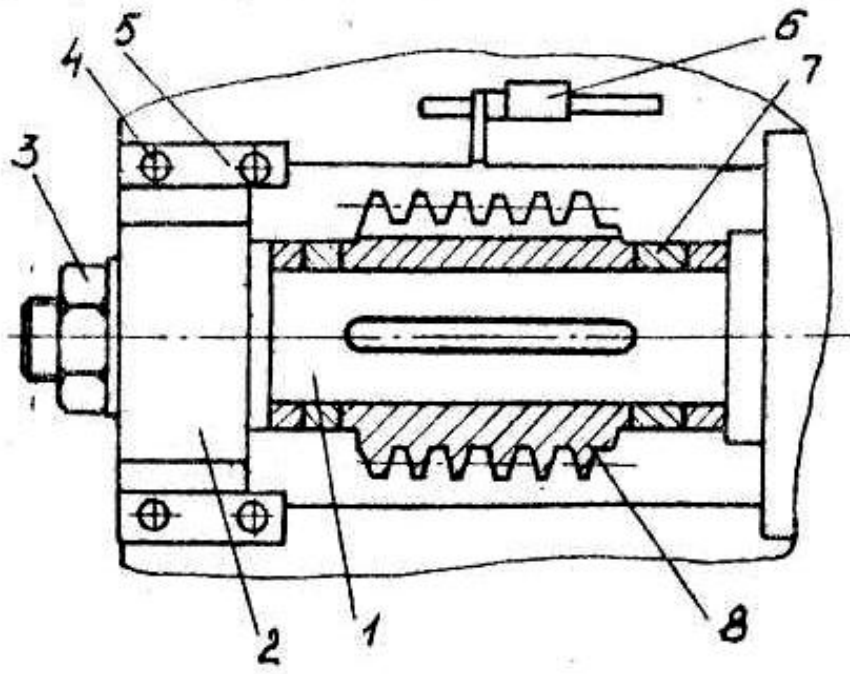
Схема встановлення черв'ячної фрези
